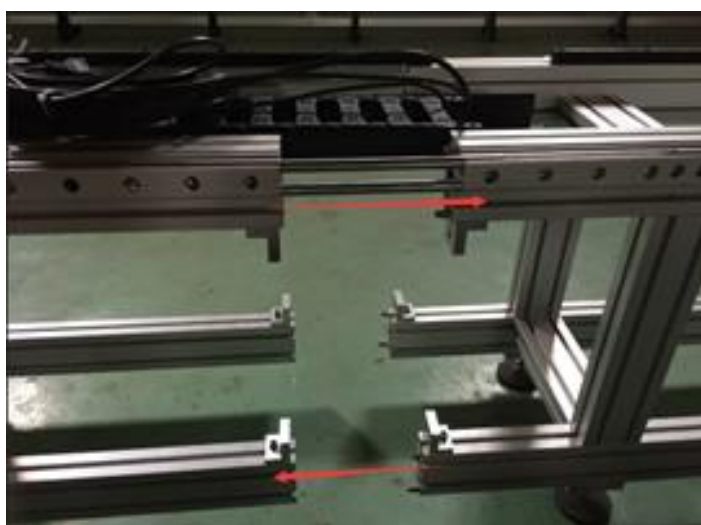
Стыковка секций 6-ти метрового станка (2500x6000)
